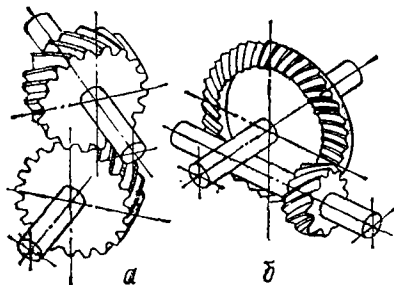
Зубчатые механизмы со скрещивающимися осями
